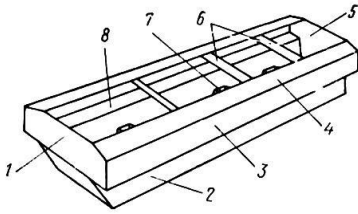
Схема корпусу: 1 – ніс; 2 – боковий борт; 3 і 4 – вертикальний і похилений борт; 5 – корма; 6 – настил; 7 – поперечина; 8 – крила
